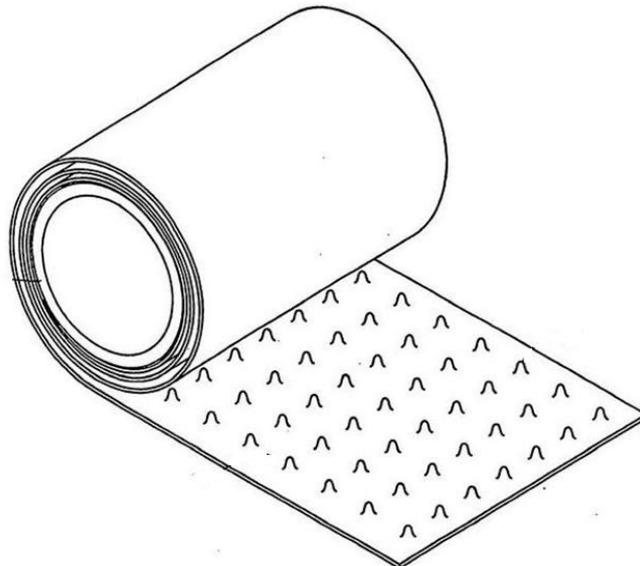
Вид заготовки для изготовления теплопередающих поверхностей пластинчатого рекуператора с луночно-штырьковыми турболизаторами
